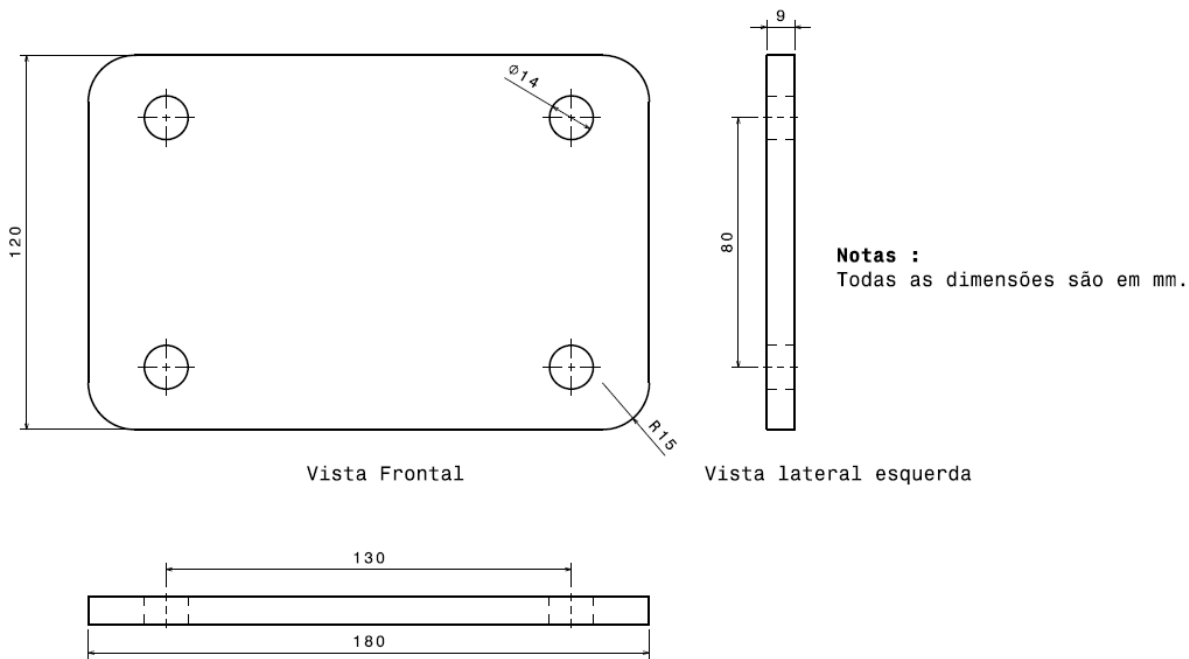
Desenho técnico para fabricação do Chapa do suporte da polia (peça fixada ao solo). (Fonte: autoria própria)
